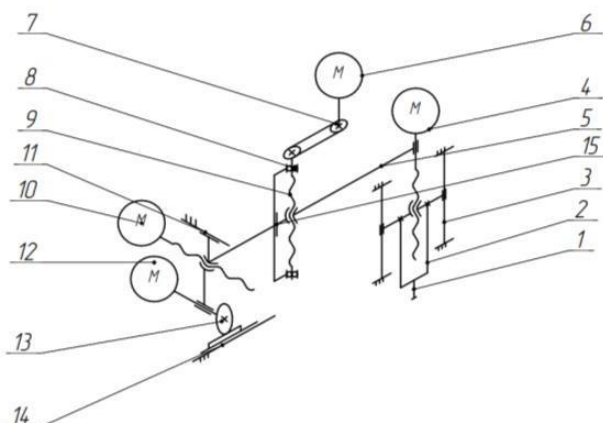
Схема кинематическая принципиальная: 1 – исполнительный орган; 2 – рамка; 3 – направляющие; 4, 6, 10, 12 – электродвигатель; 5 – кронштейн; 7 – зубчато-ременная передача; 8 – подшипник; 9 – винтовая передача; 11, 14, 15 – направляющая; 13 – ременная передача
